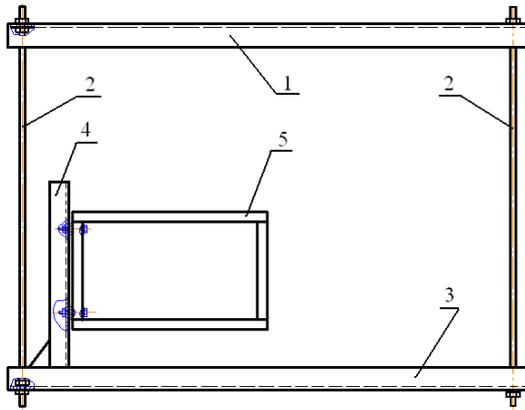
Схема приспособления для установки объекта испытаний на стенд:
